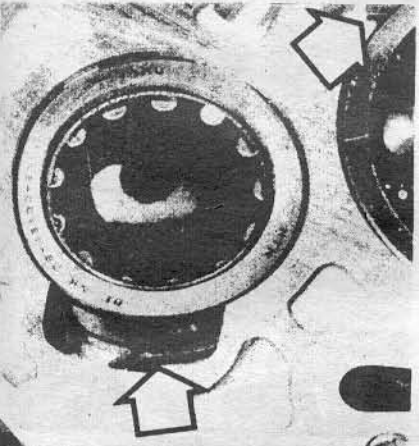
Разожмите стопорные кольца и вставьте подшипники вторичного и промежуточного валов.
